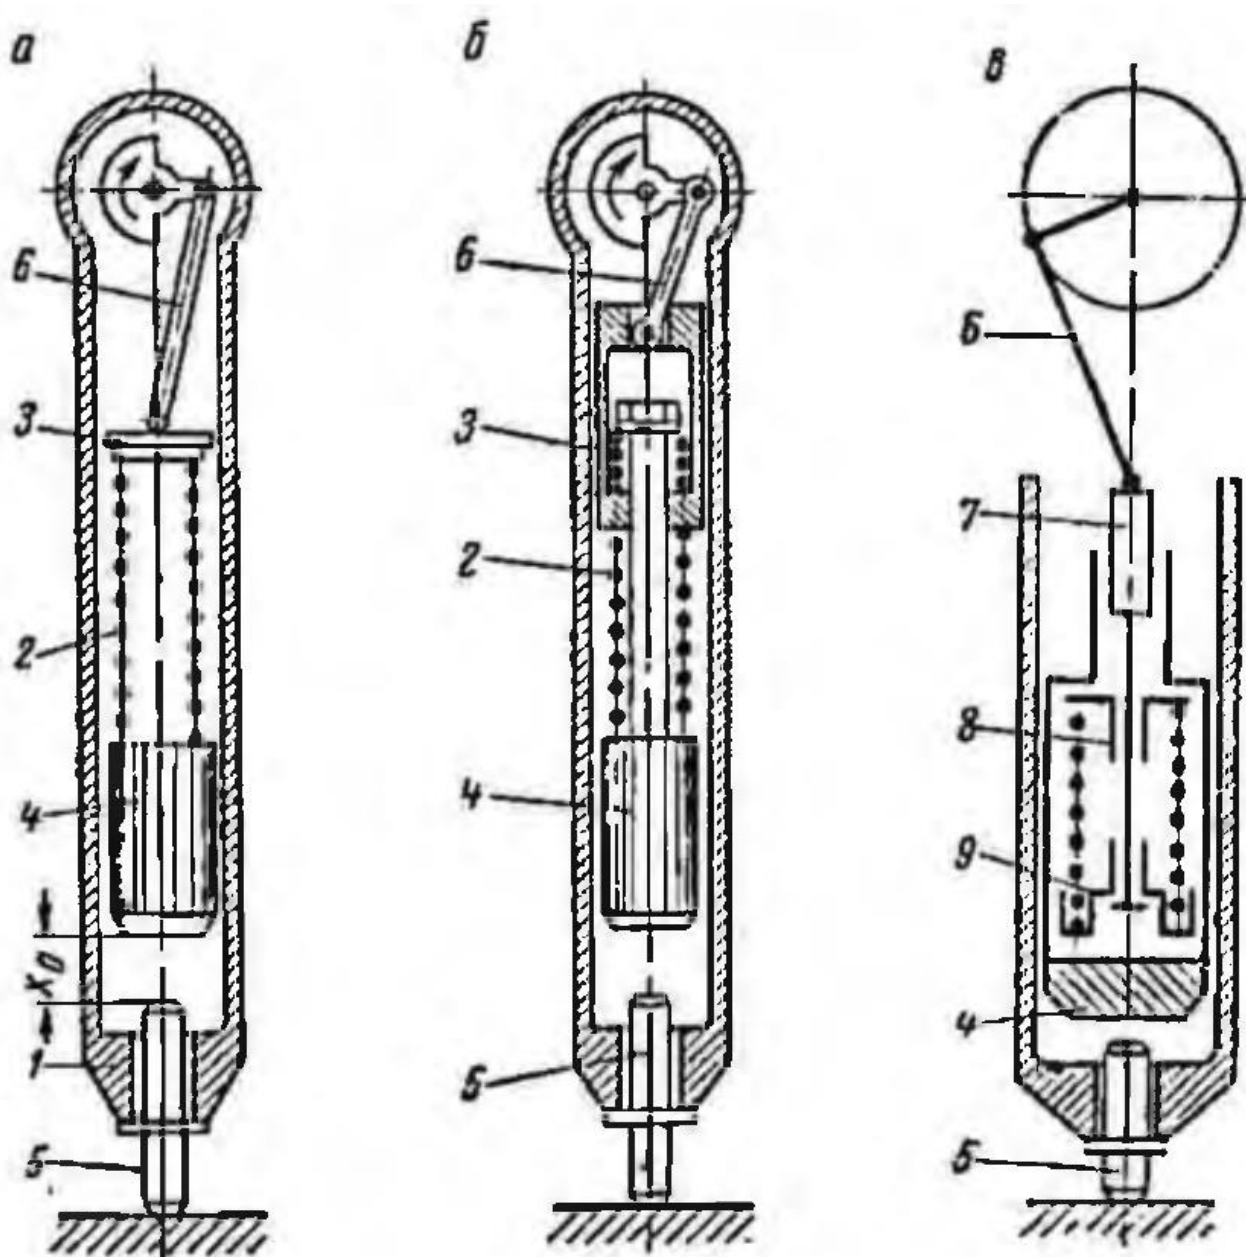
Схеми пружних ударних механізмів з гнучким зв'язком бойка [13]: 1 – корпус; 2 – пружина; 3 – ползун; 4 – бойок; 5 – робочий інструмент; 6 – кривошипно-шатунний механізм; 7 – шток; 8 – верхня оправка; 9 – нижня оправка
